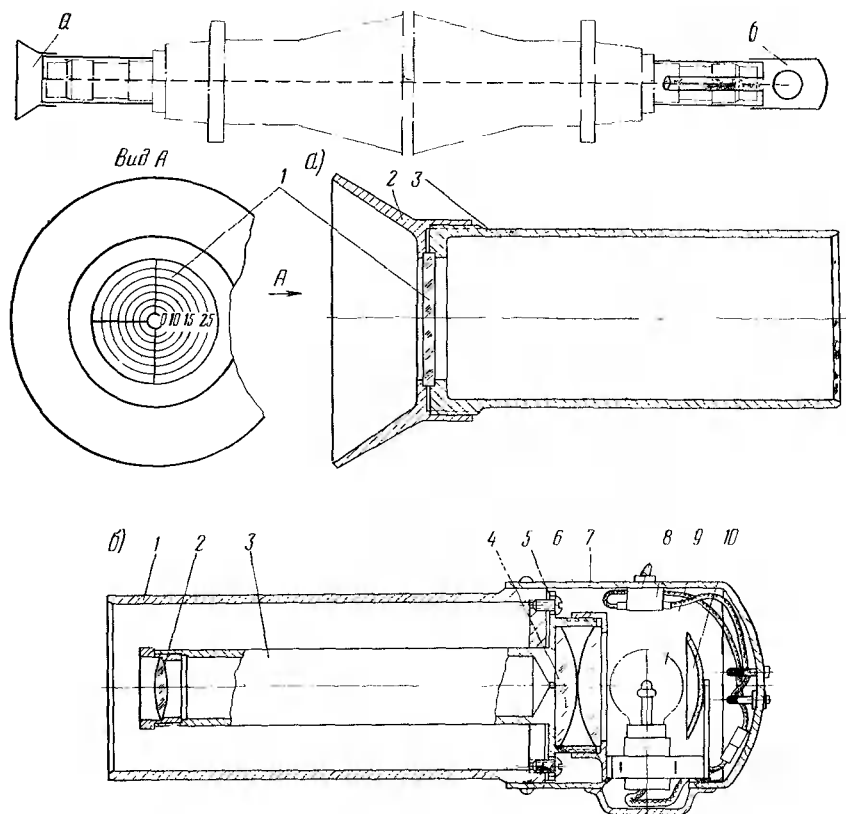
Прибор для контроля соосности кожухов полуосей:
